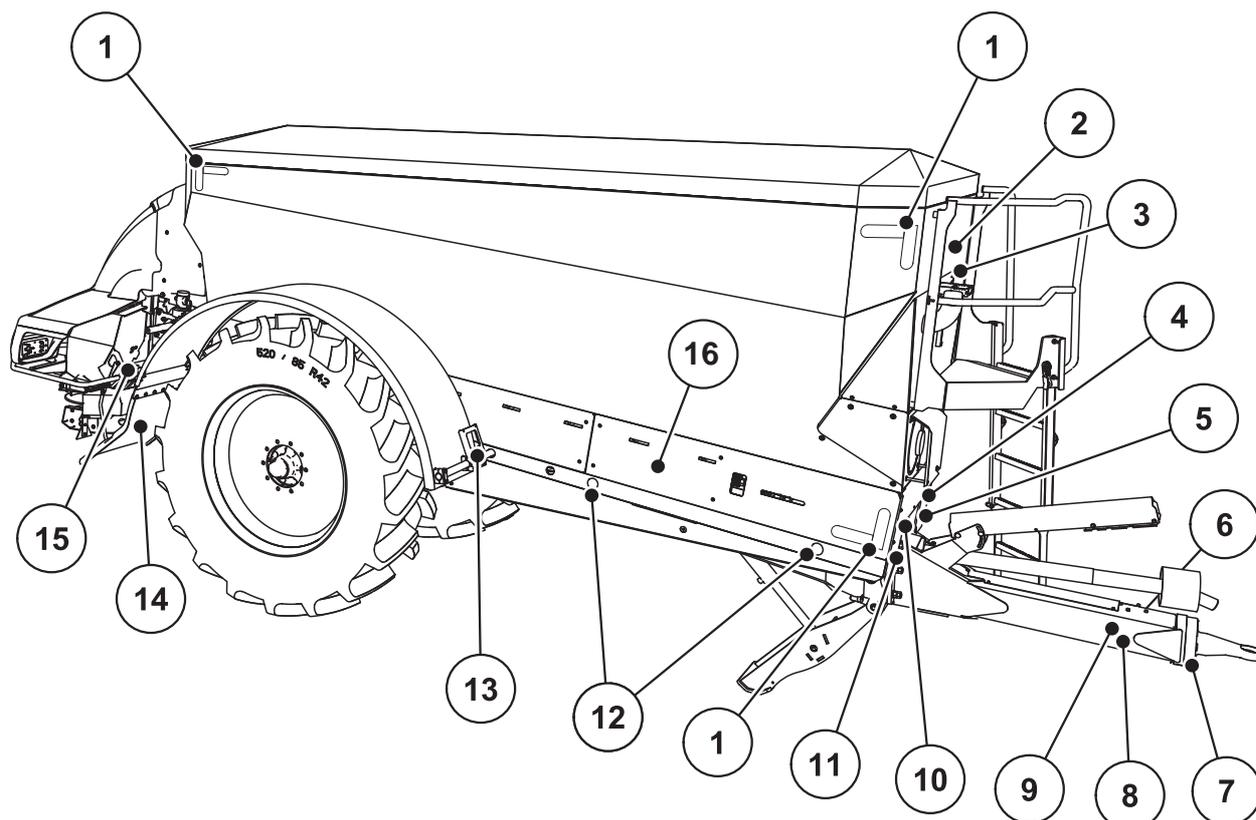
Расположение защитных приспособлений, предупредительных указаний и инструкций сбоку машины
